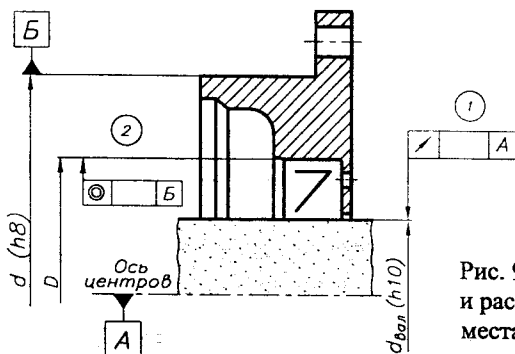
Допуски формы и расположения поверхностей места установки манжеты
